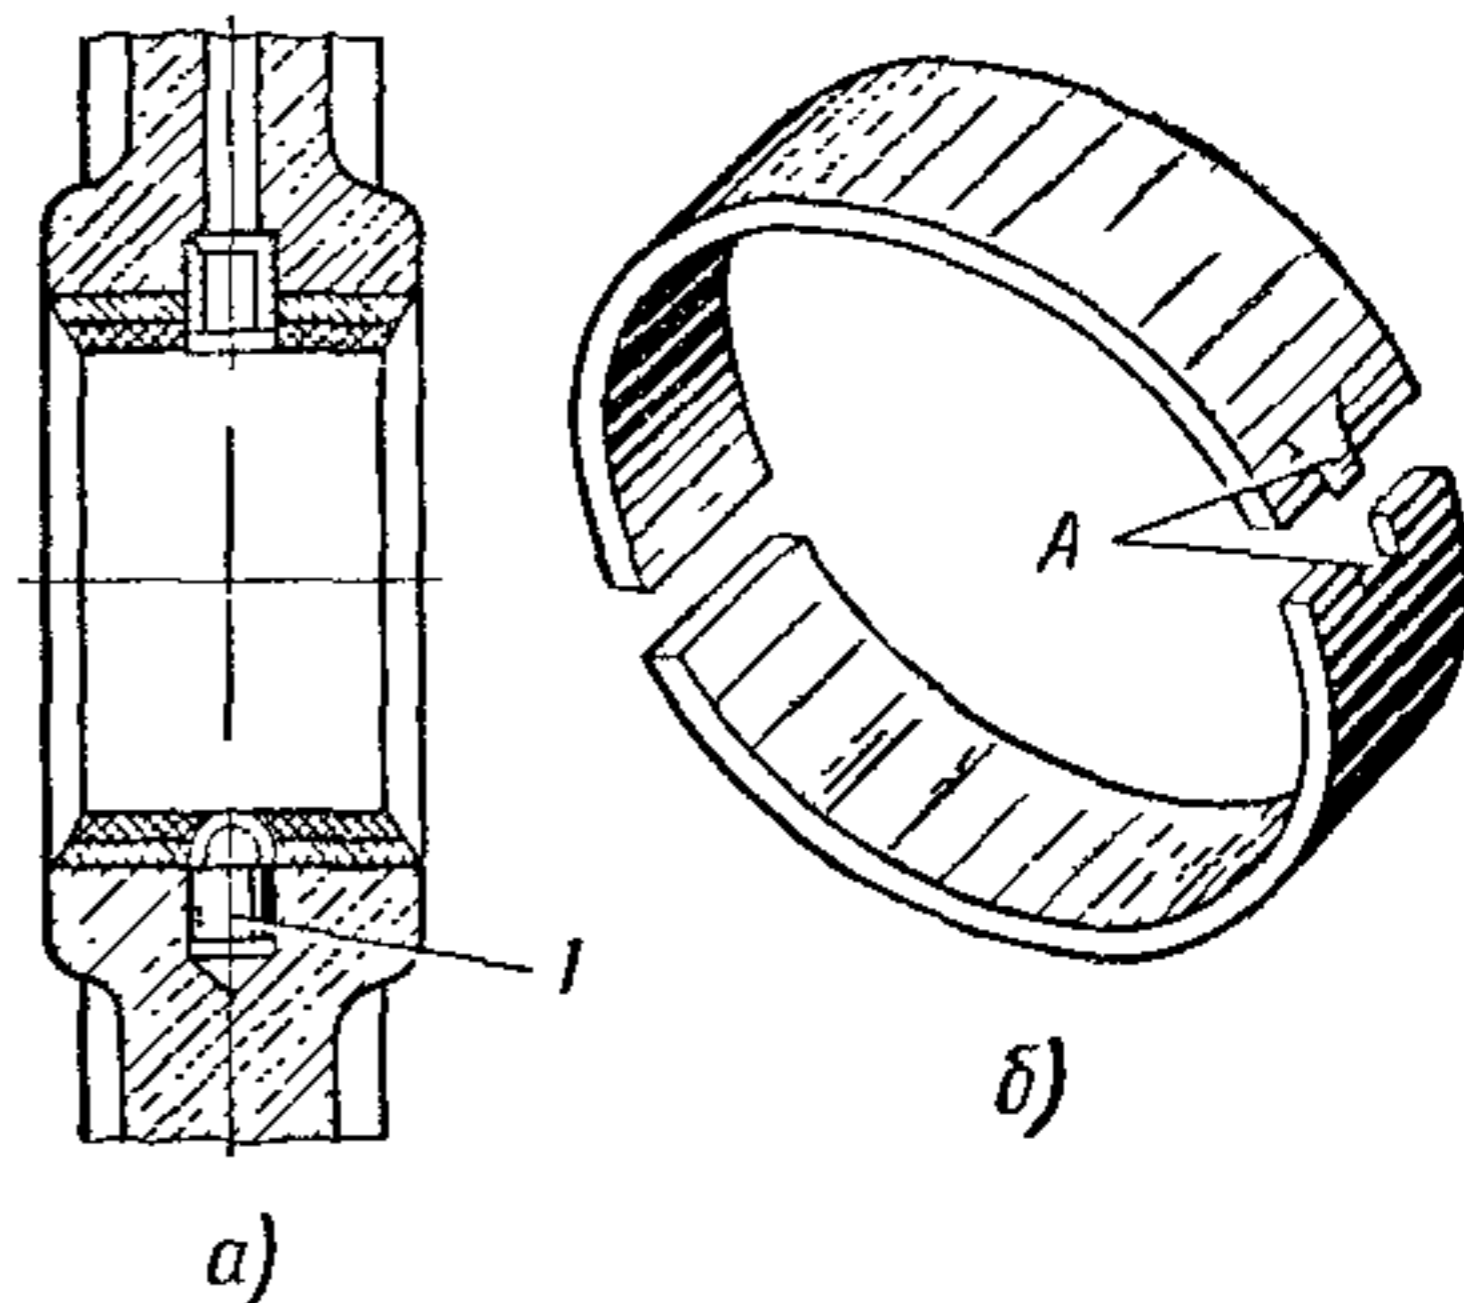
Способы фиксации вкладышей коренных подшипников:
